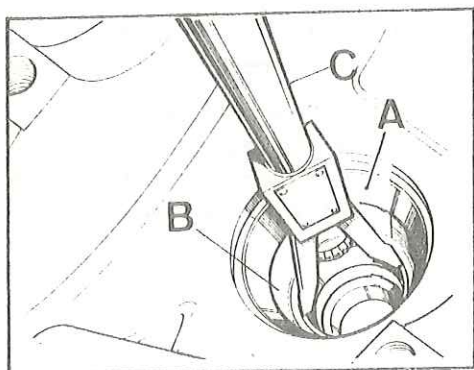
Desmontaje a presión de las pistas de los cojinetes
